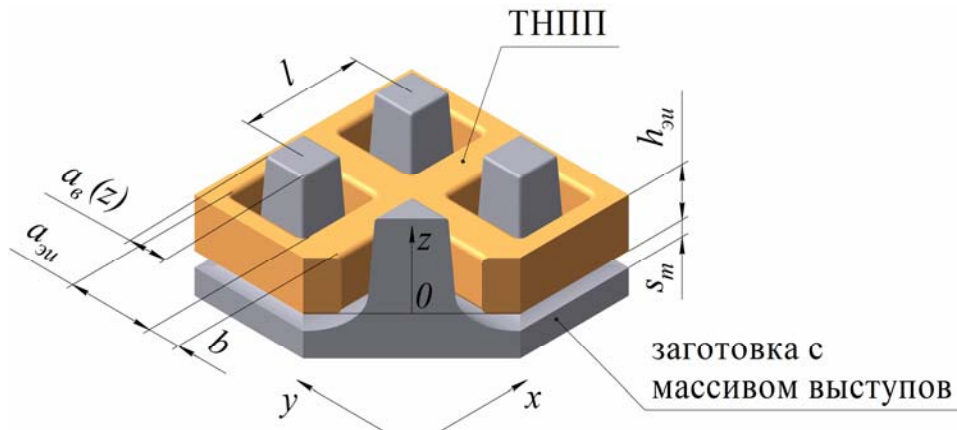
Схема простановка размеров на ТНПП и заготовке с вырезаемыми выступами
